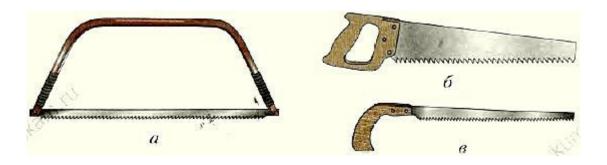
Инструменты для пиления: а — лучковая пила; б — столярная ножовка; в — выкружная пила
